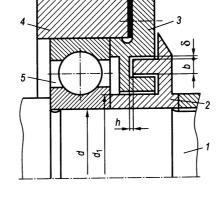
Лабиринтное комбинированное уплотнение: 1 – вал; 2 – втулка; 3 – крышка; 4 – корпус; 5 – подшипник
